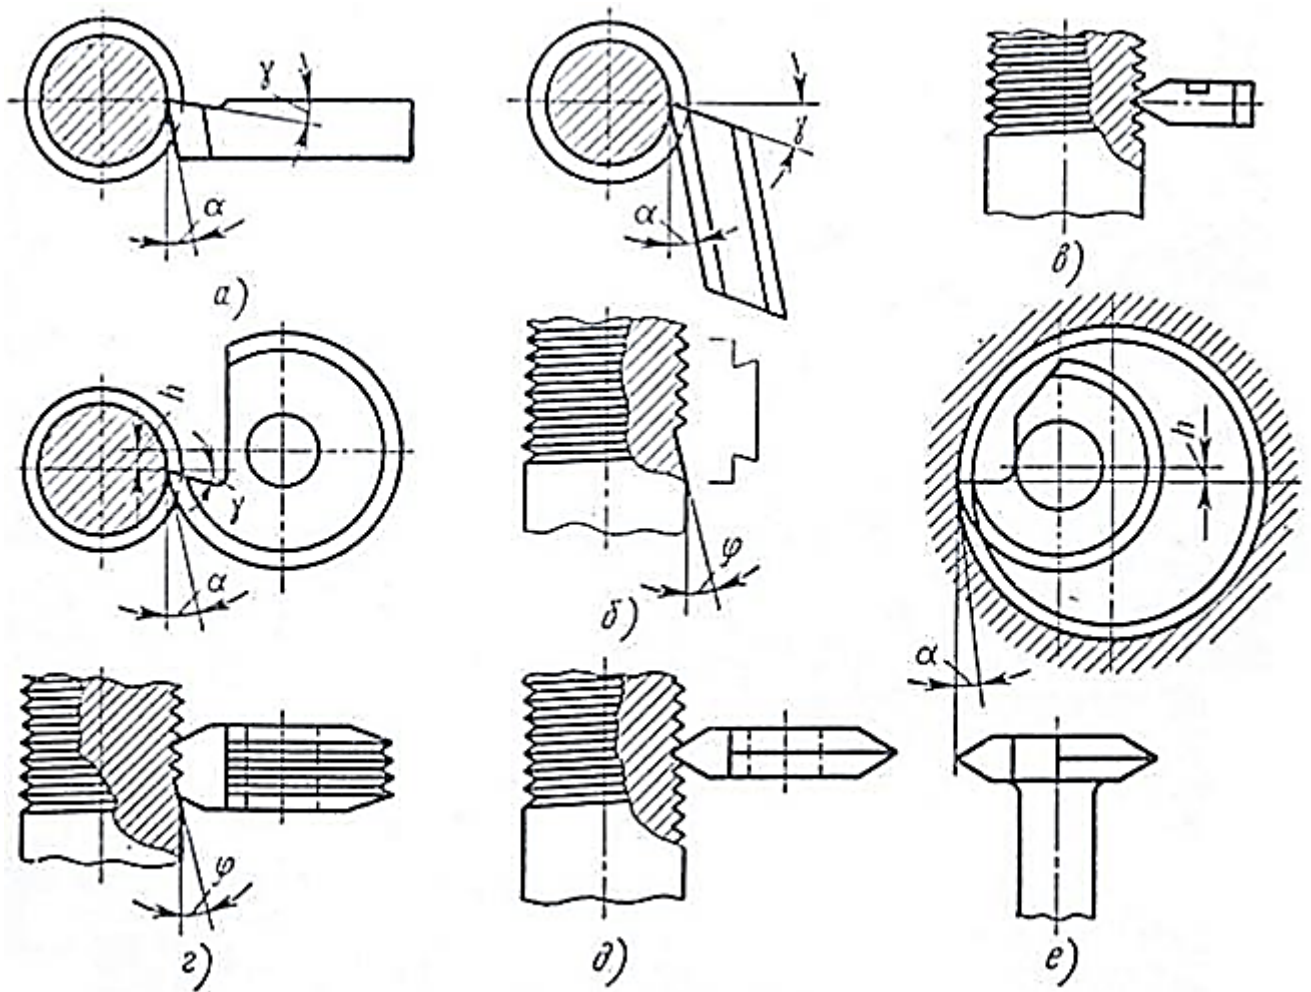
Різці для нарізування різьби: а — стрижневий; б — призматичний багатпрофільний; в — призматичний однопрофільних; г — дисковий багатпрофільний; д — дисковий однопрофільних; е — дисковий для внутрішньої різьби; α — задній кут; φ — передній кут; γ — кут забірнього конуса; h — висота установки осі різця
